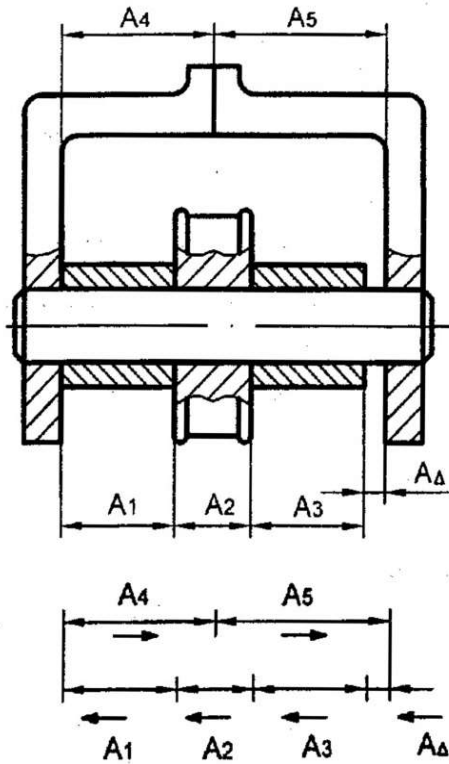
Эскиз узла схемы сборочной размерной цепи
